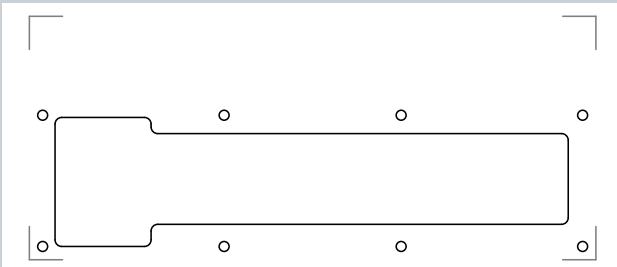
→ DXF-Vorlage für Kontur Schaltschrankausschnitt mit Befestigungsbohrungen für Ventilinsel VTUG
